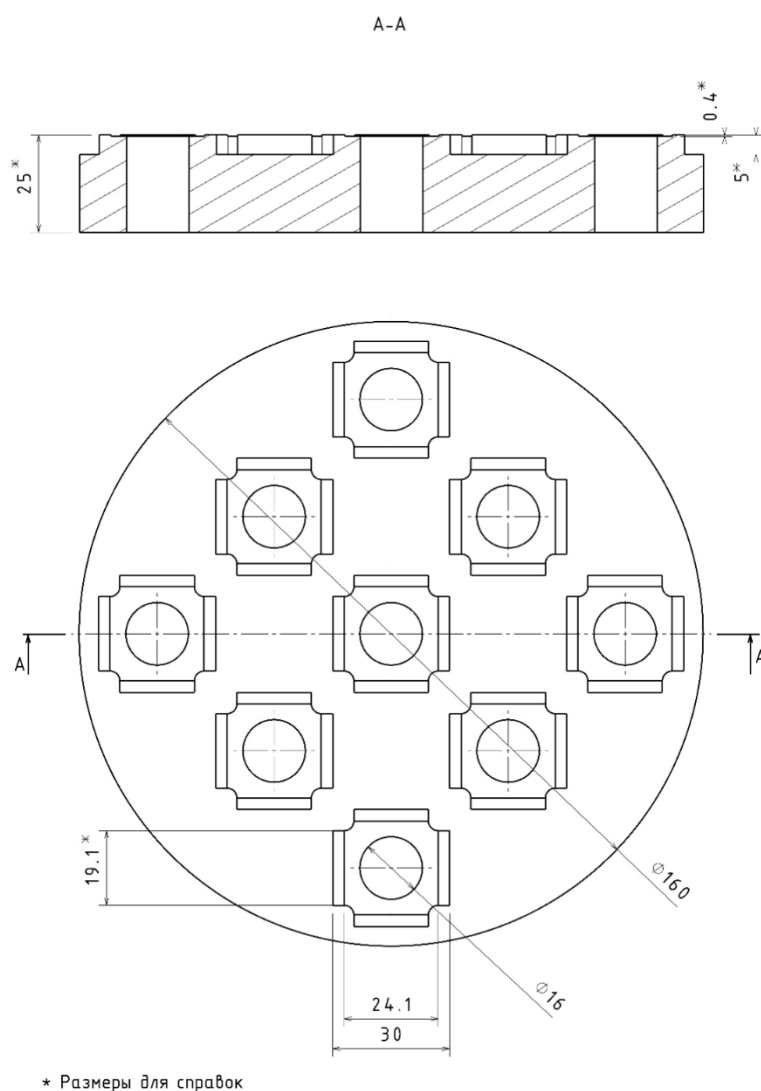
Эскизный рисунок общего вида приспособления для вакуумного стола с одновременным размещением девяти заготовок
